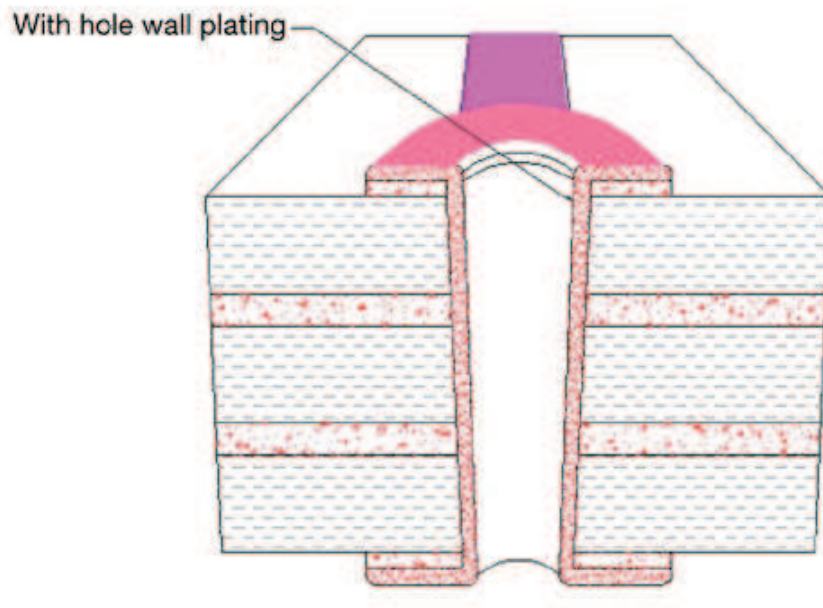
Vista Transversal de una Perforación Platinada [5].
